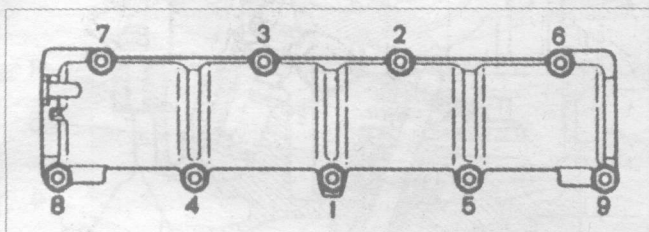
Порядок подтягивания гаек крепления корпуса подшипников распределительного вала
